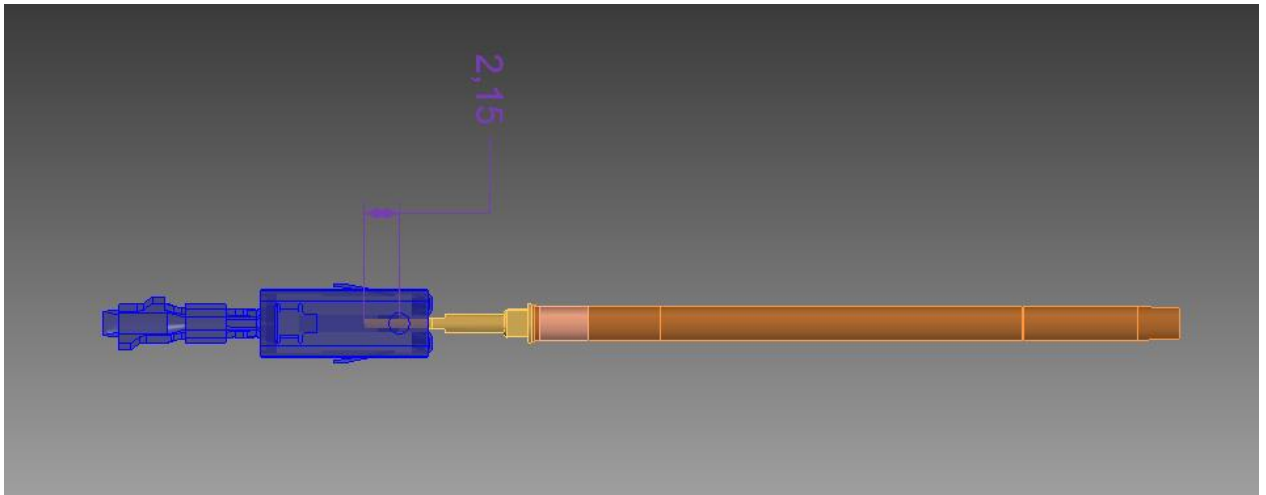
Imagen de traslape entre pin de prueba plano y terminal de conector
